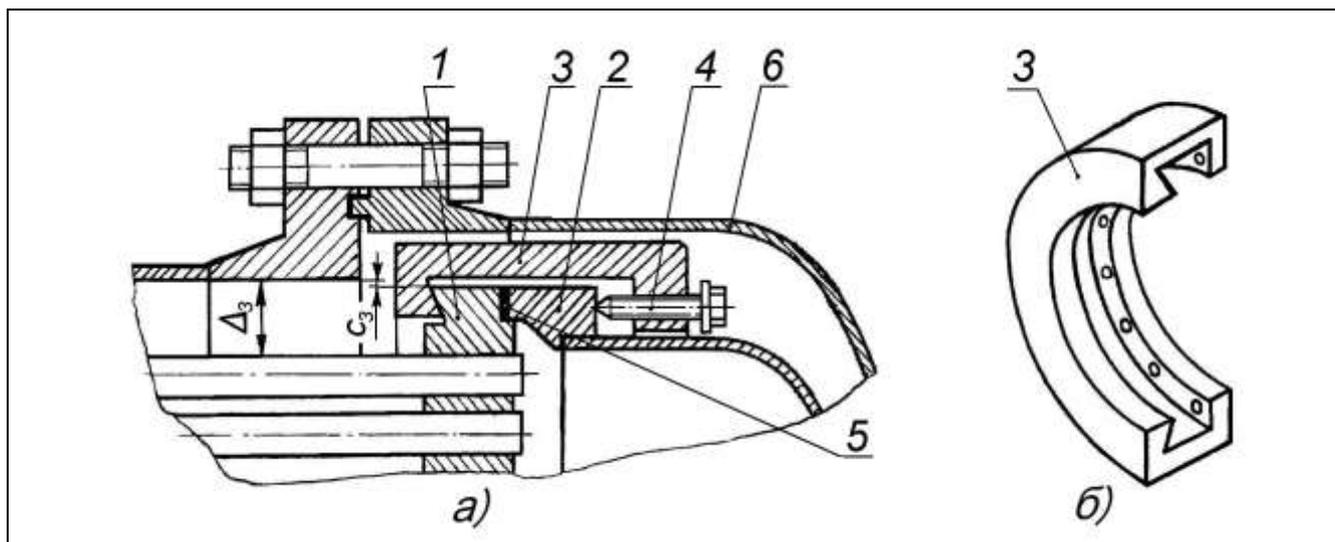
Плавающая головка с разрезной фланцевой скобой 3 типа «Алко»: а) – общий вид плавающей головки в сборе; б) – внешний вид левой половины разрезной фланцевой скобы 3 до начала сборки аппарата
